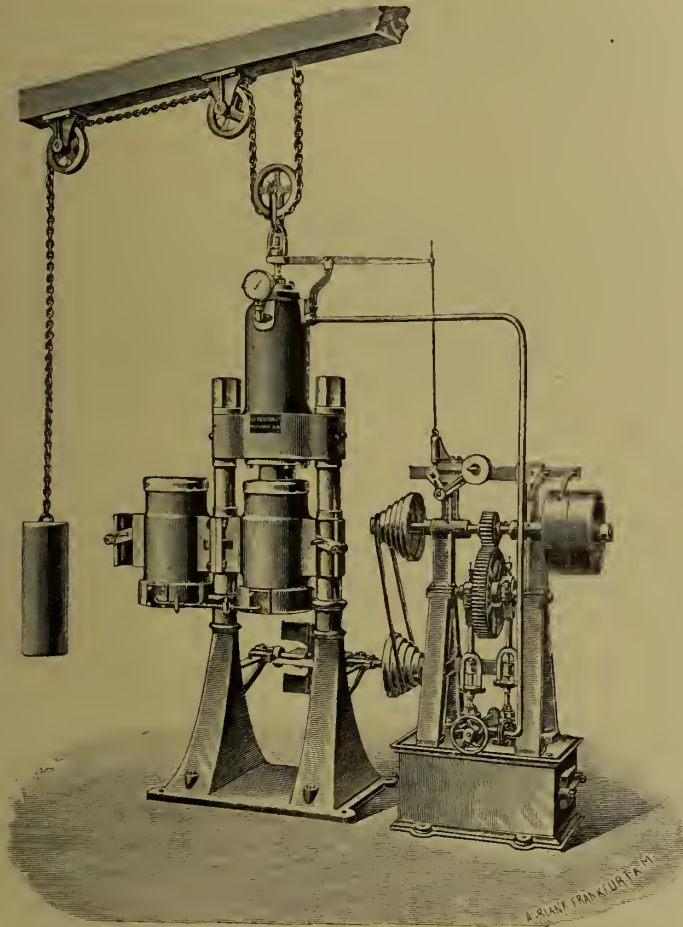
Hydraulische Presse von Mehger & Co., Homburg v. d. G.
